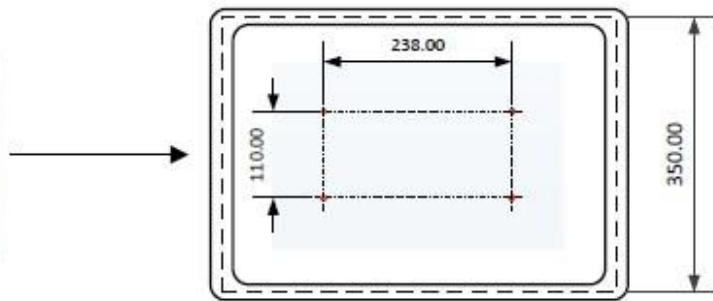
Ubicación de perforaciones para fijación de batería auxiliar
